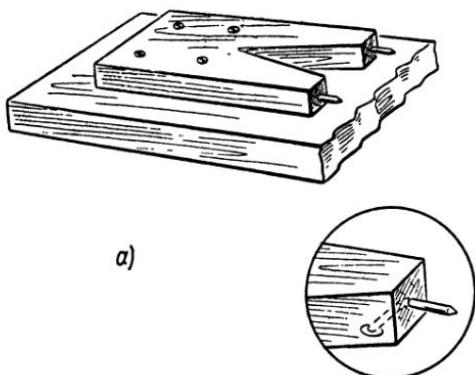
Приспособления для крепления доски на крышке стелюги:
